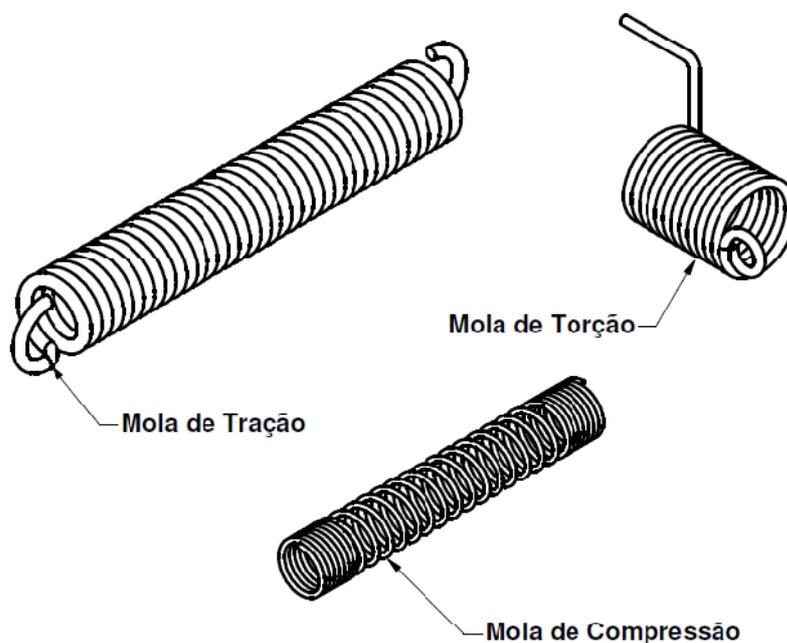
Desenho Técnico Ilustrativo do Produto Fabricado pela Empresa
